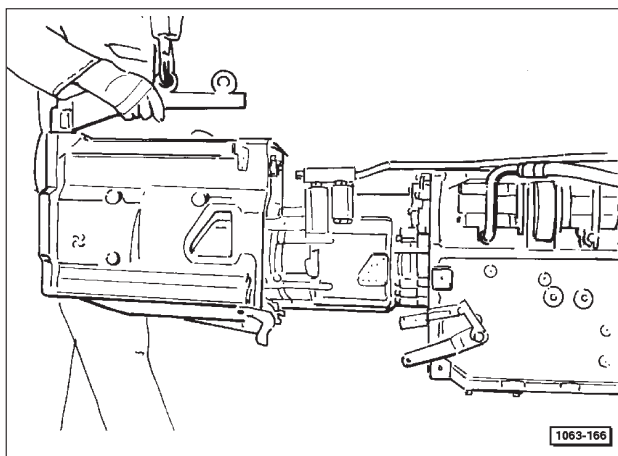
À l'aide d'un palan, accoupler le carter avant au carter arrière.
